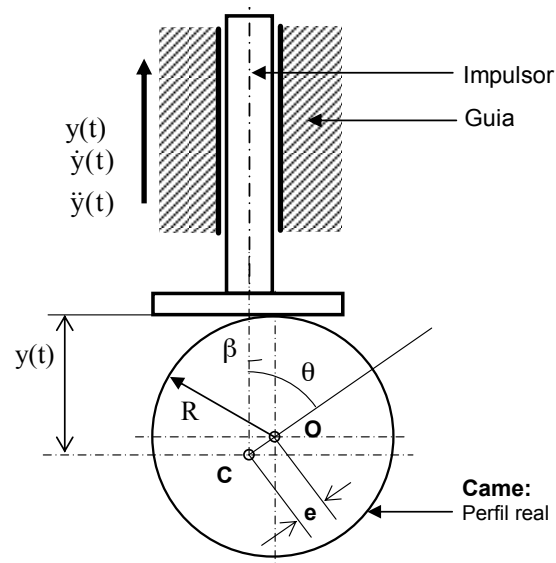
Came circular excêntrica harmónica simples com impulsor de prato
